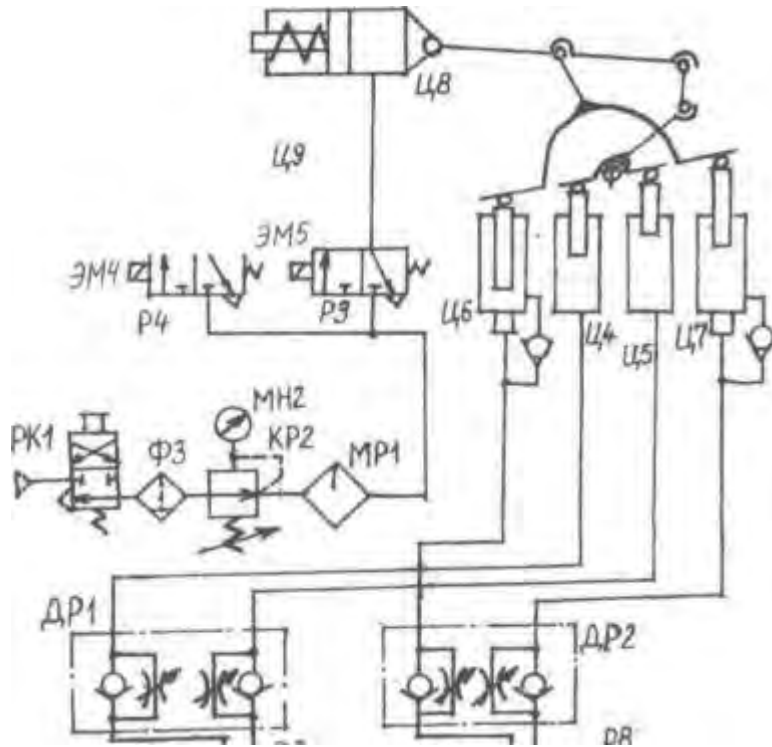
Гидропневматическая схема манипулятора для съема отливок
